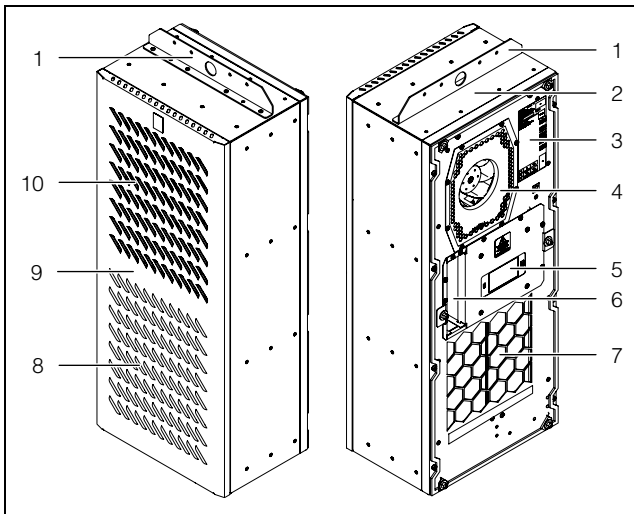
Hauptkomponenten des Kühlgeräts (SK 3485330)
